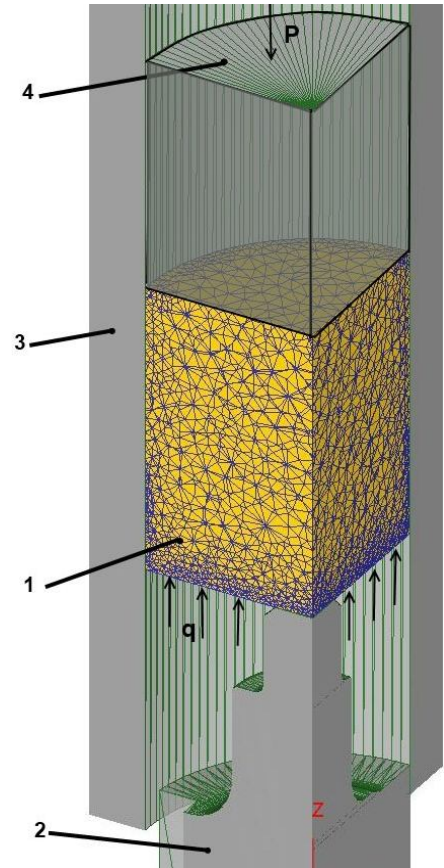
Розрахункова схема видавлювання порожнини прессформи в умовах дії протитиску на позаконтактну поверхню заготовки.
